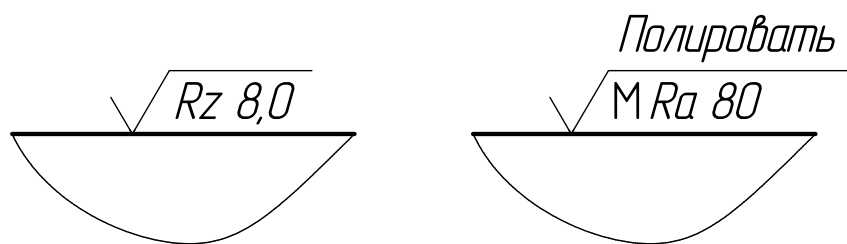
Примеры обозначения шероховатости поверхности
